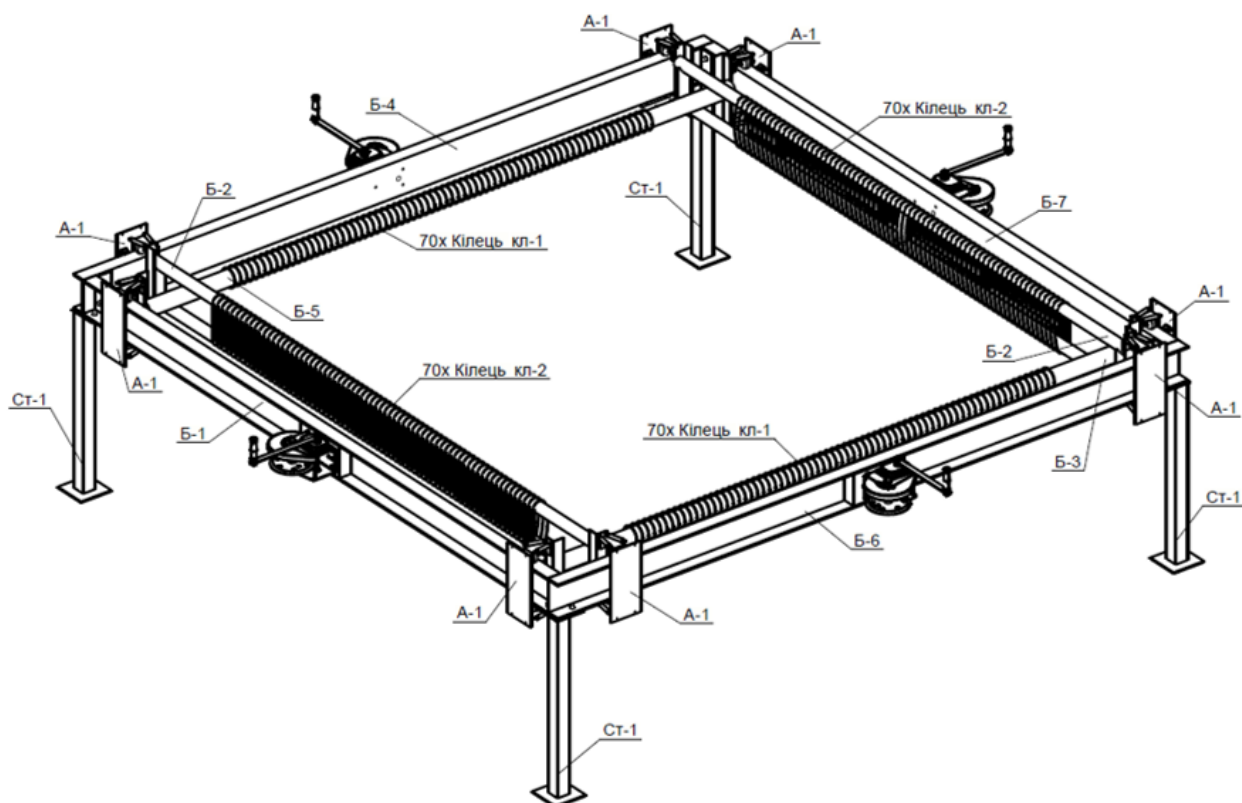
Загальний вигляд випробувального стенда для сітки (фрагмент робочого креслення з позначенням елементів: Б-1...Б-7 – балки рами; А-1 – напрямні елементи роликів; Ст-1 – сталеві стояки-опори тощо)
